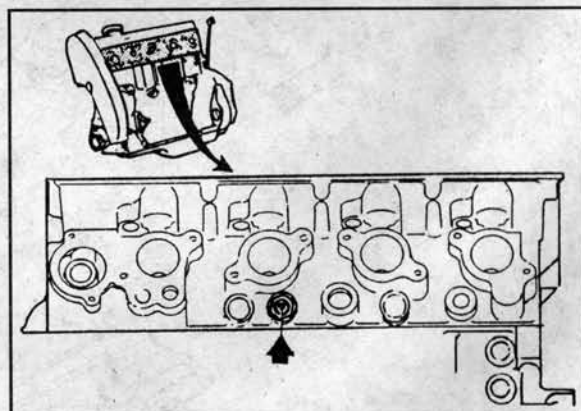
Расположение датчика температуры охлаждающей жидкости в головке блока цилиндров двигателя В19
